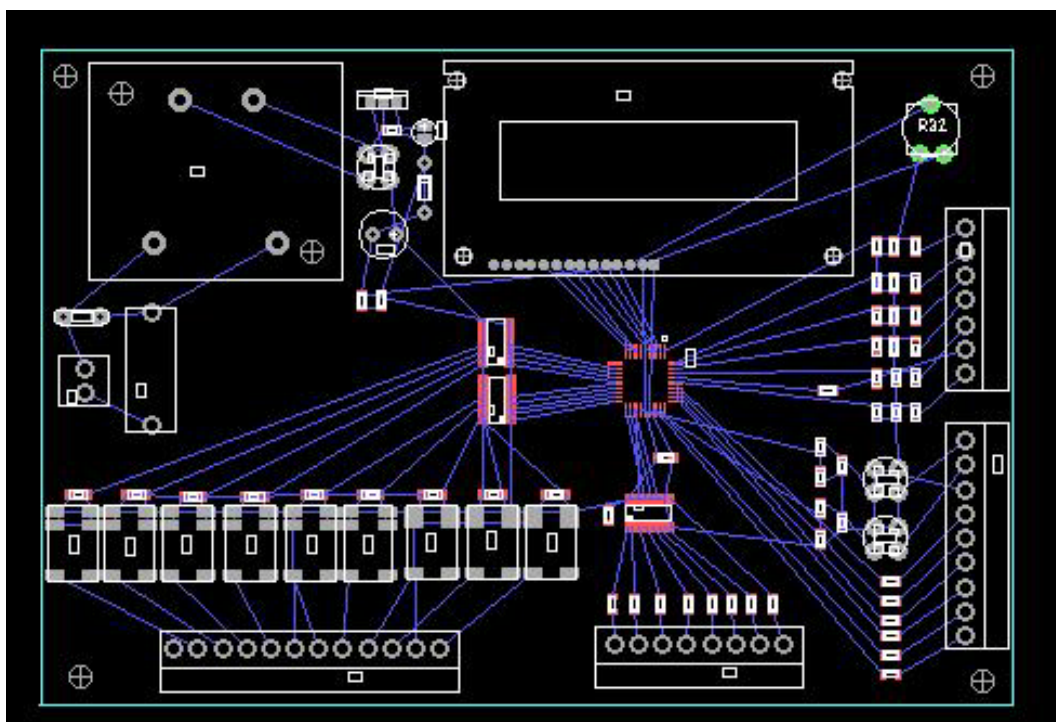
Impressió pantalla PCB amb els components distribuïts
